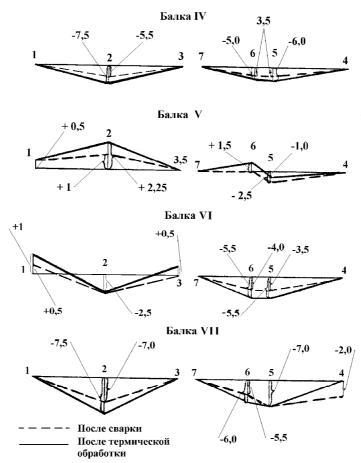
Схема измерения величины прогиба в балках IV–VII после сварки и термической обработки
